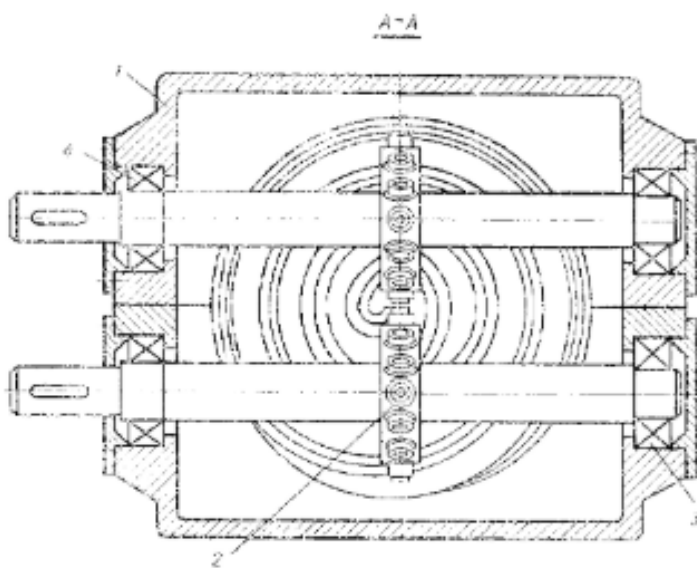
Привод валков прокатного стана (Разрез А-А)
